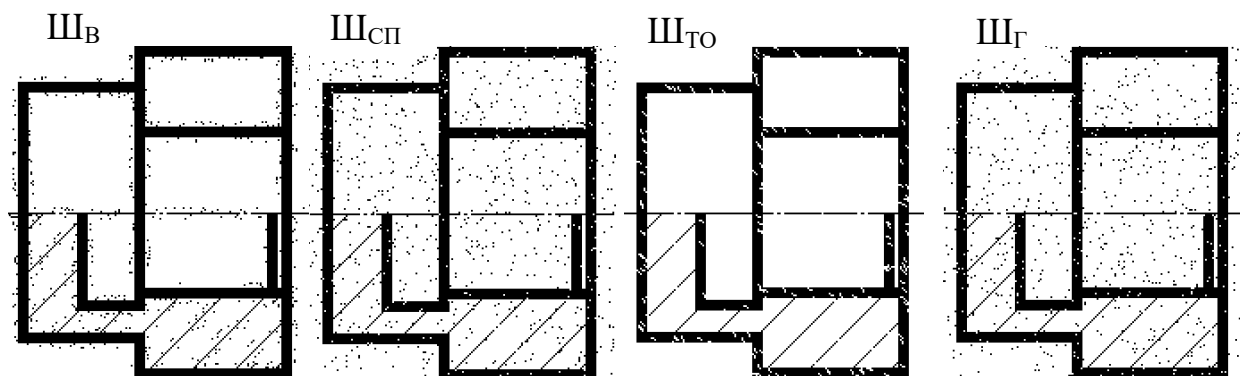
Приклади типових спотворень бінарного зображення креслення деталі
